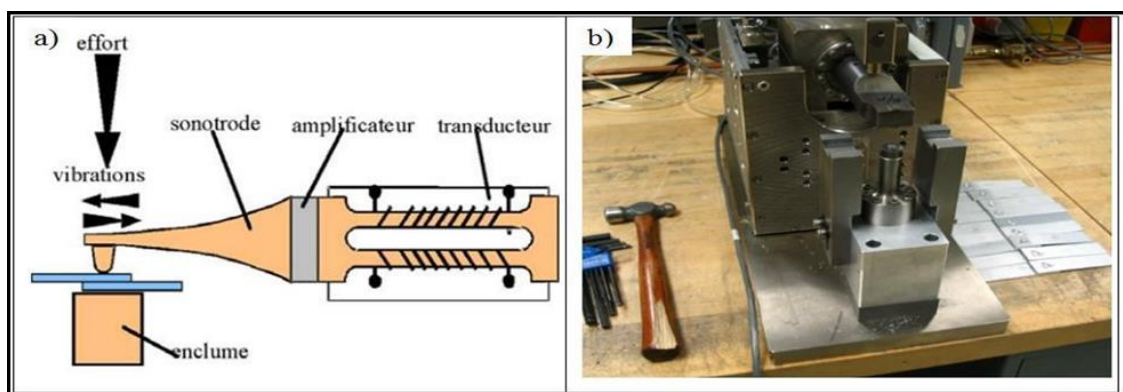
Soudage par ultrasons. a) schéma du procédé b) machine de soudage.
